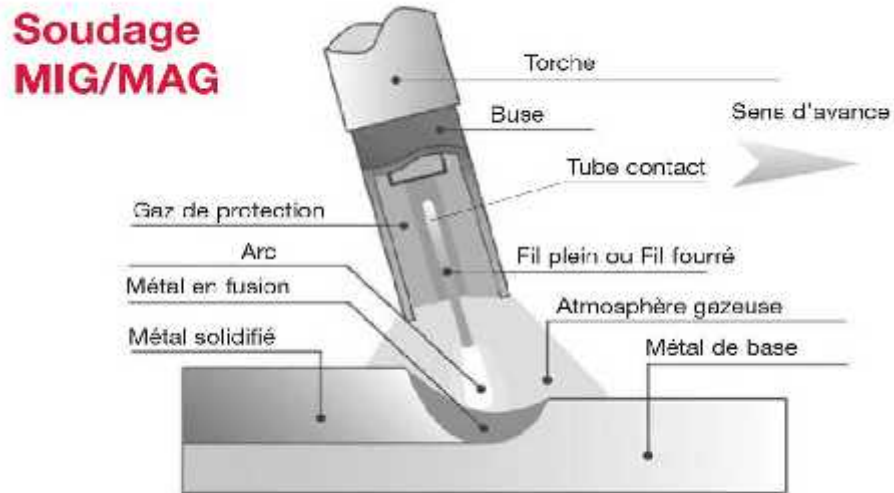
Procédé de soudage MIG/MAG
